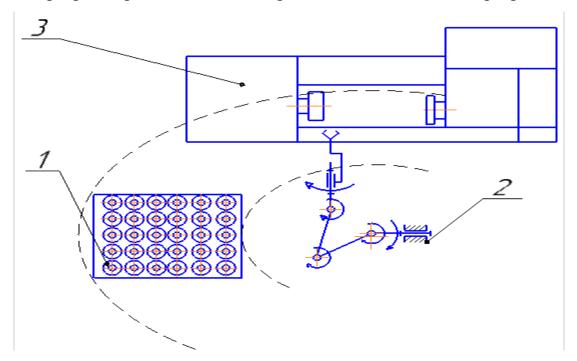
Схема автоматизированной ячейки токарного станка с ЧПУ:
